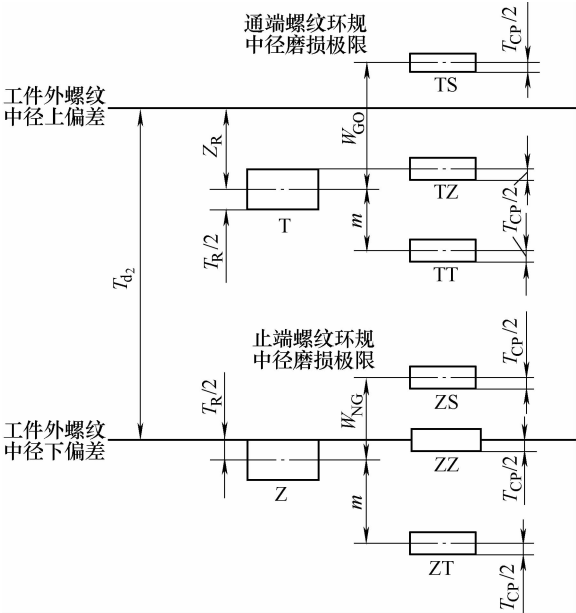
检验工件外螺纹用的螺纹环规和螺纹环规用的校对螺纹塞规中径公差带图
